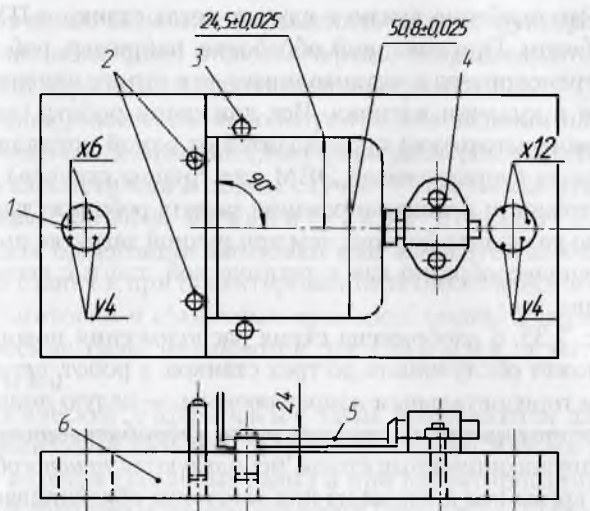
Специальное приспособление для обработки заготовок типа «угольник» на станках с ЧПУ
